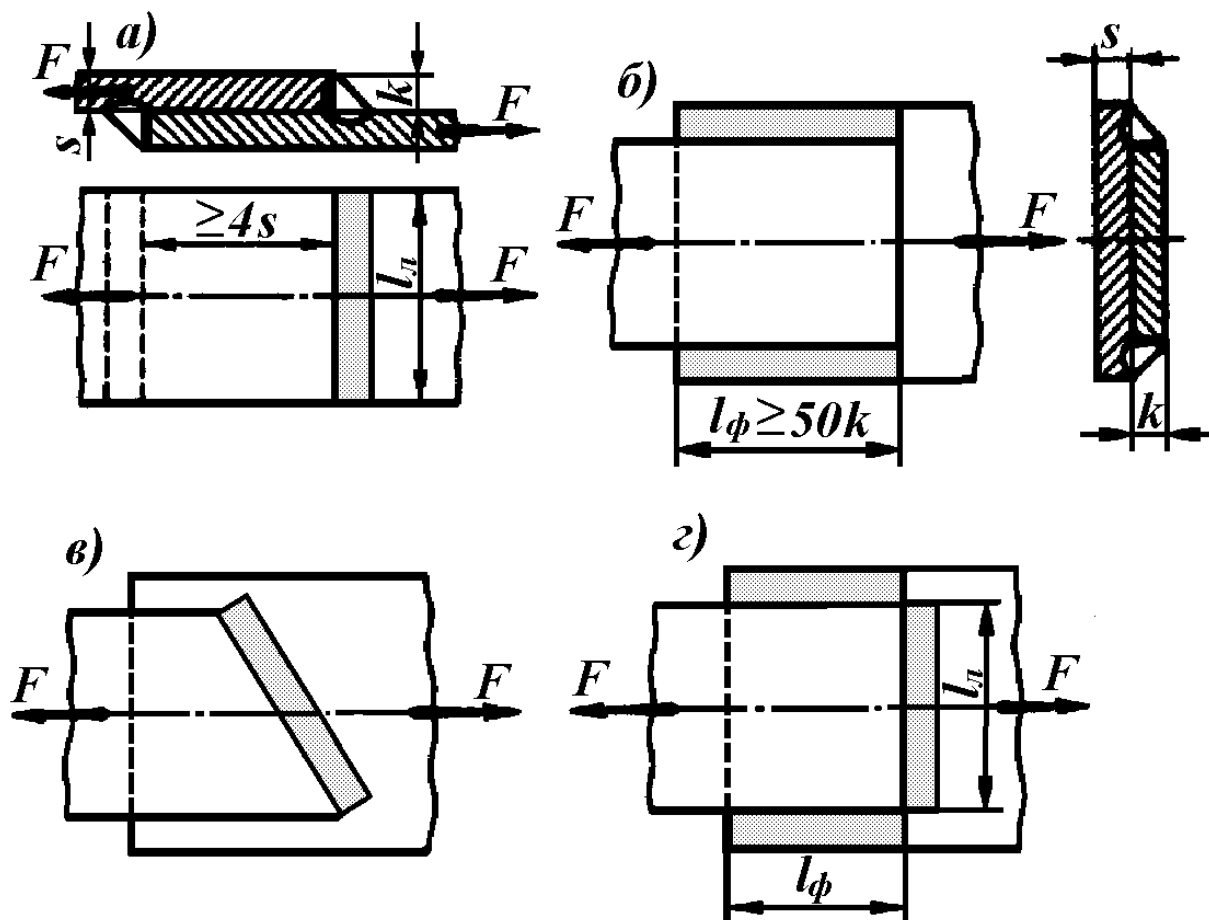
Сварные соединения пластин внахлест:
